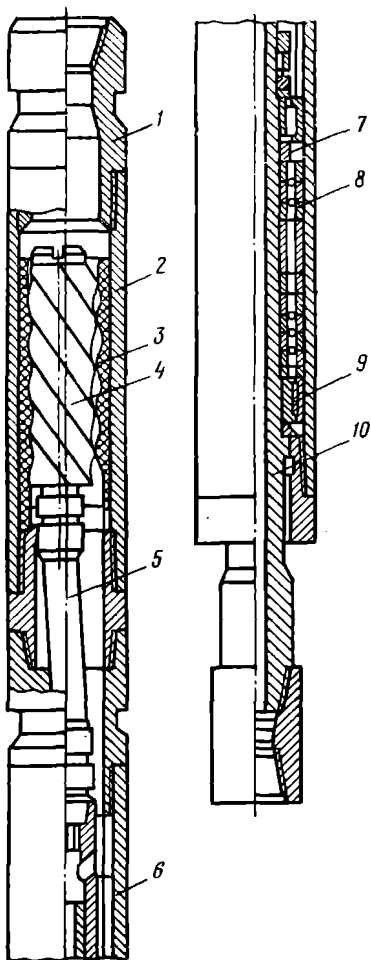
Конструкция винтового двигателя Д2-172:
